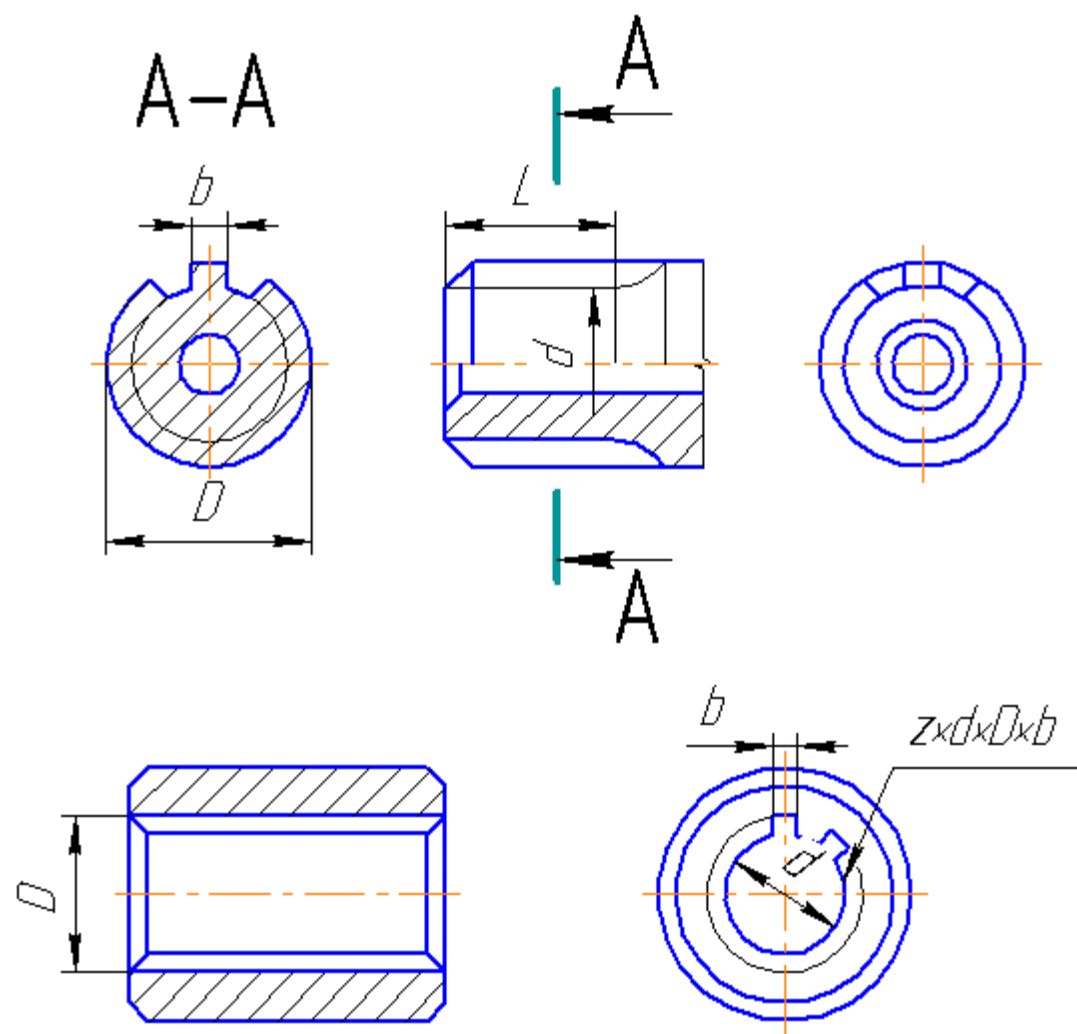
Пример детали со шлицевым хвостовиком и фрагменты чертежей деталей
